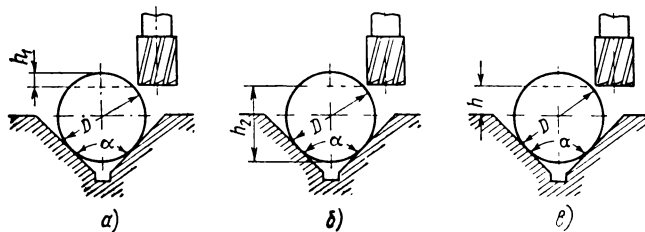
Схемы установки вала на призму для фрезерования площадки, когда за измерительную базу принята:
